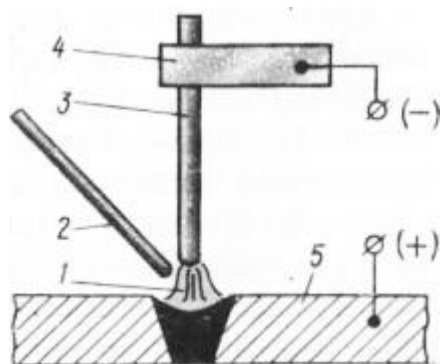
Схема сварки по способу Бенардоса Н. Н.: 1 — электрическая дуга; 2 — присадочный пруток; 3 — угольный электрод; 4 — держатель; 5 — свариваемый металл.
